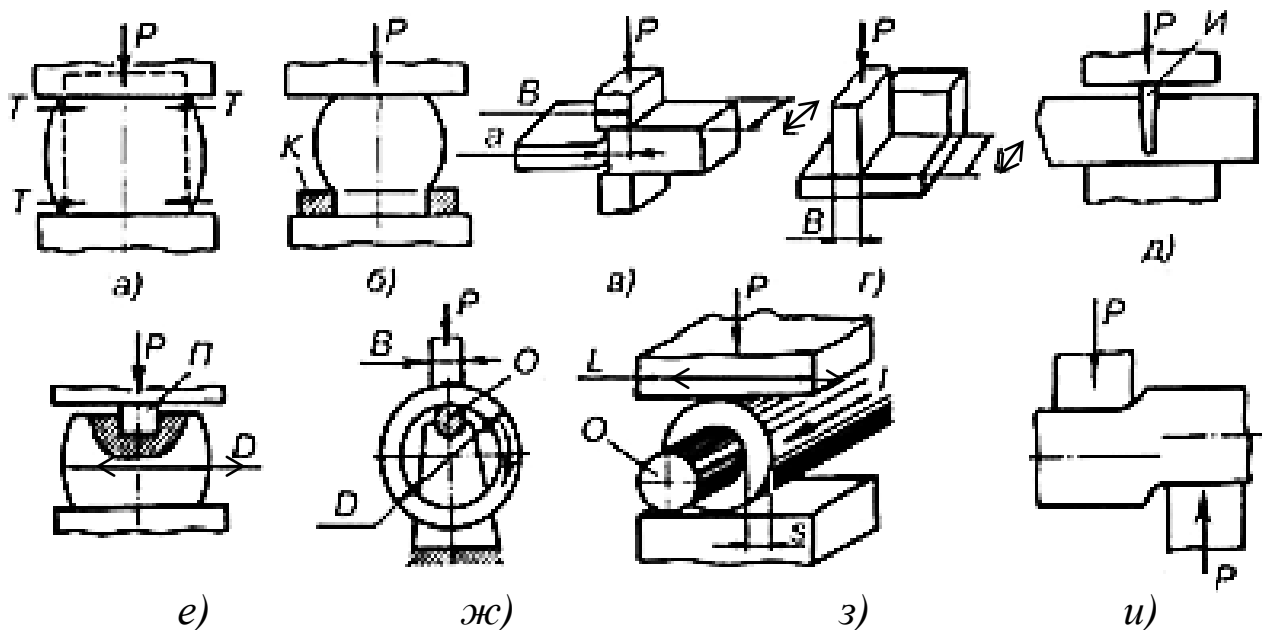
Операции свободнойковки: а – осадка; б – высадка; в – протяжка; г – разгонка; д – рубка; е – прошивка; ж – раскатка; з – протяжка на оправке; и – передача; P – нагрузка; T – силы трения; K – кольцо; $И$ – инструмент; $П$ – прошивень; O – оправка; B – ширина бойка; L – участок заготовки; s – толщина стенки заготовки
